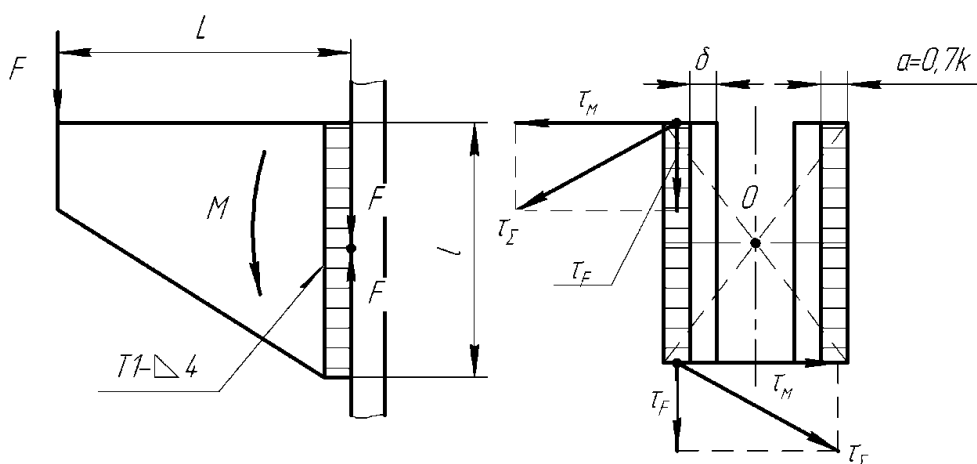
Расчетная схема сварного соединения угловыми швами
